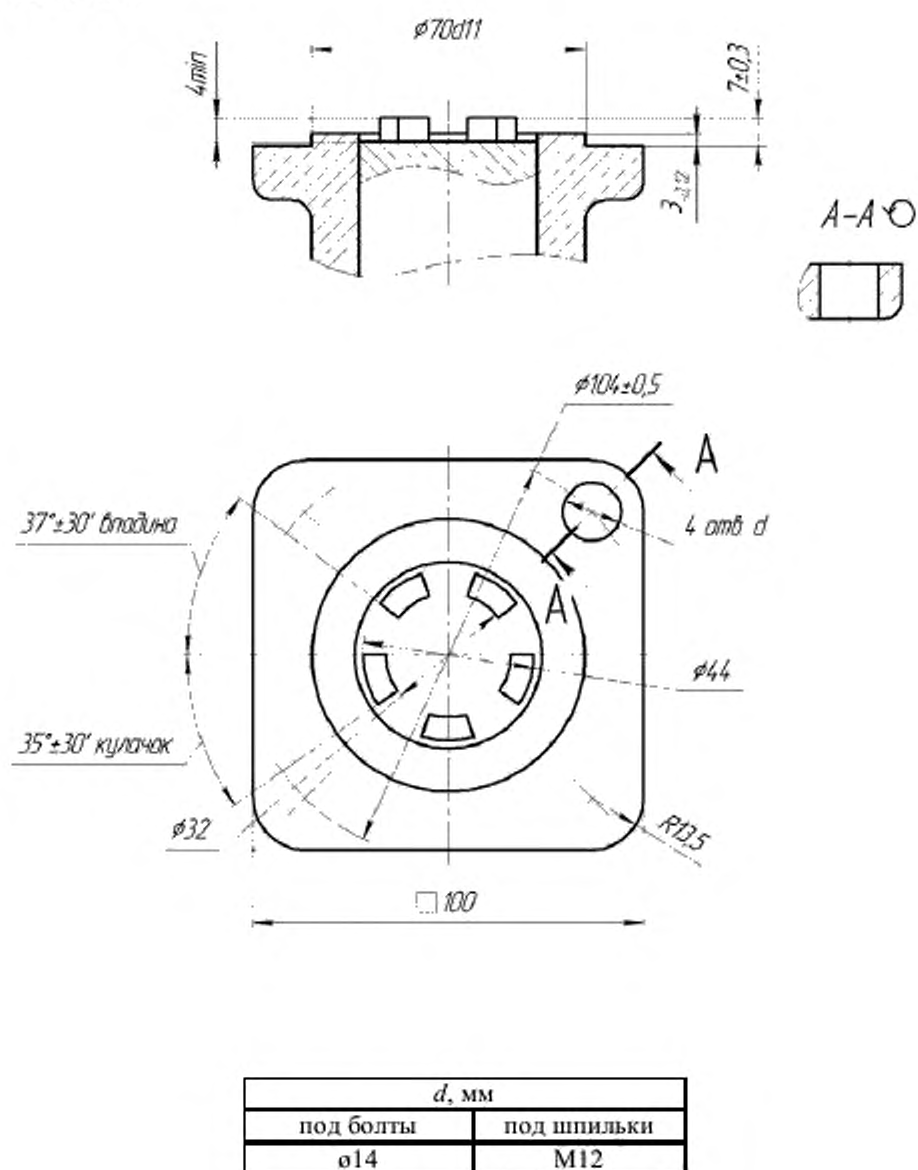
Ответное присоединение трубопроводной арматуры типа АК
